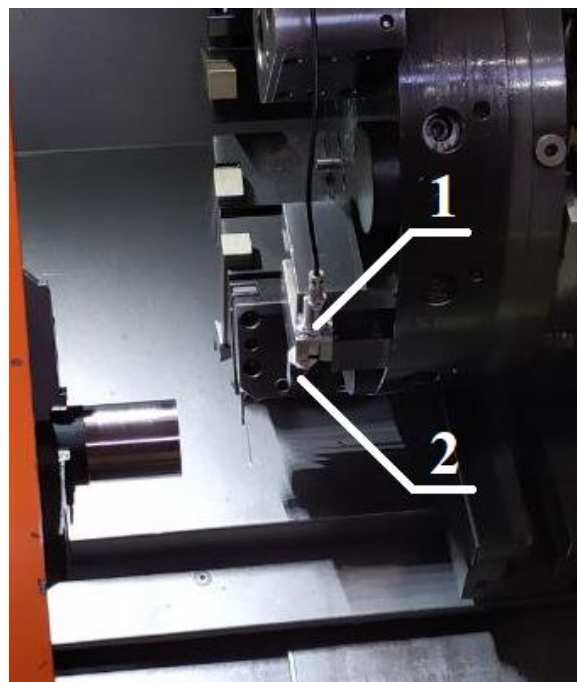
Расположение вибродатчика на державке сборного резца в револьверном барабане станка с ЧПУ Viktor VTurn 26: 1 – акселерометр, 2 – резец
